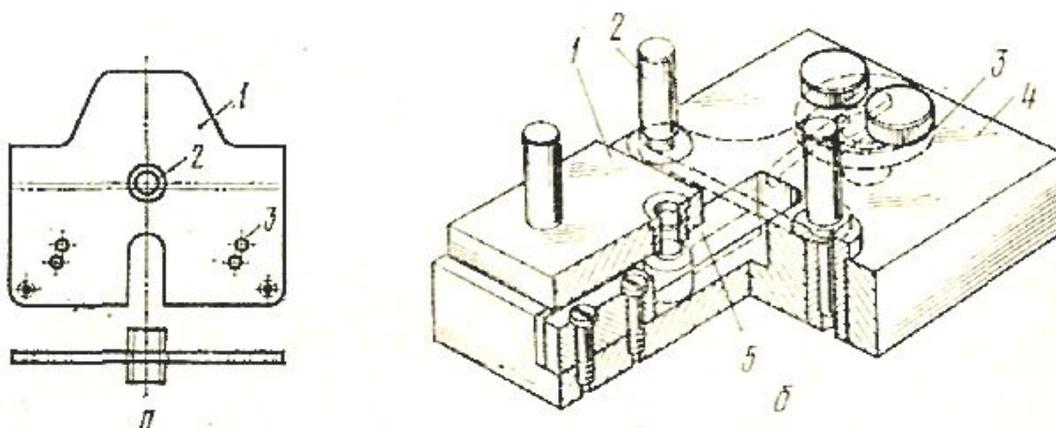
Приспособления для ремонта (а) и контроля (б) водила
